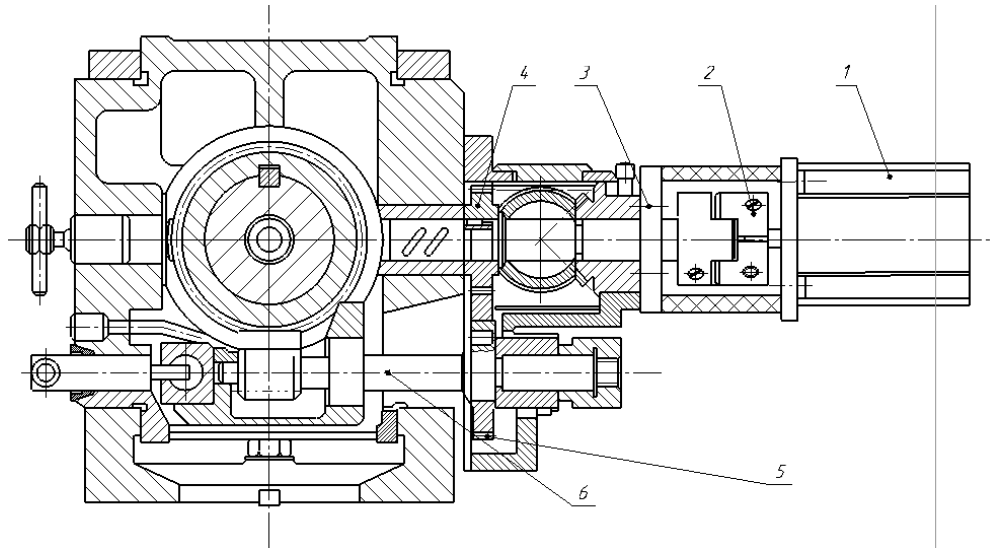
Вигляд перетину конструкції модернізованої ділильної головки УДГ-160: 1 - кроковий двигун NEMA23; 2 – муфта; 3 – корпус; 4 – колесо зубчасте; 5 – ведена шестерня; 6 - черв'як
